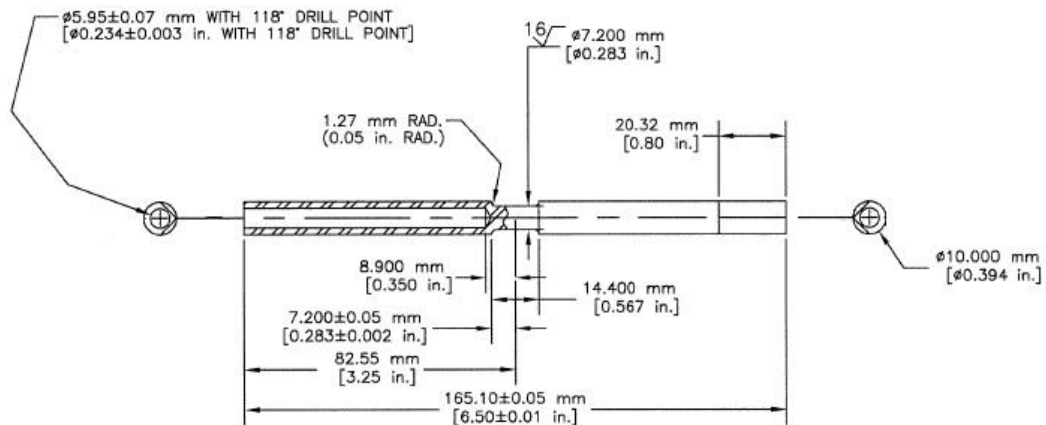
Probeta de 10 mm para ensayo de torsión en caliente en máquina Gleeble.
